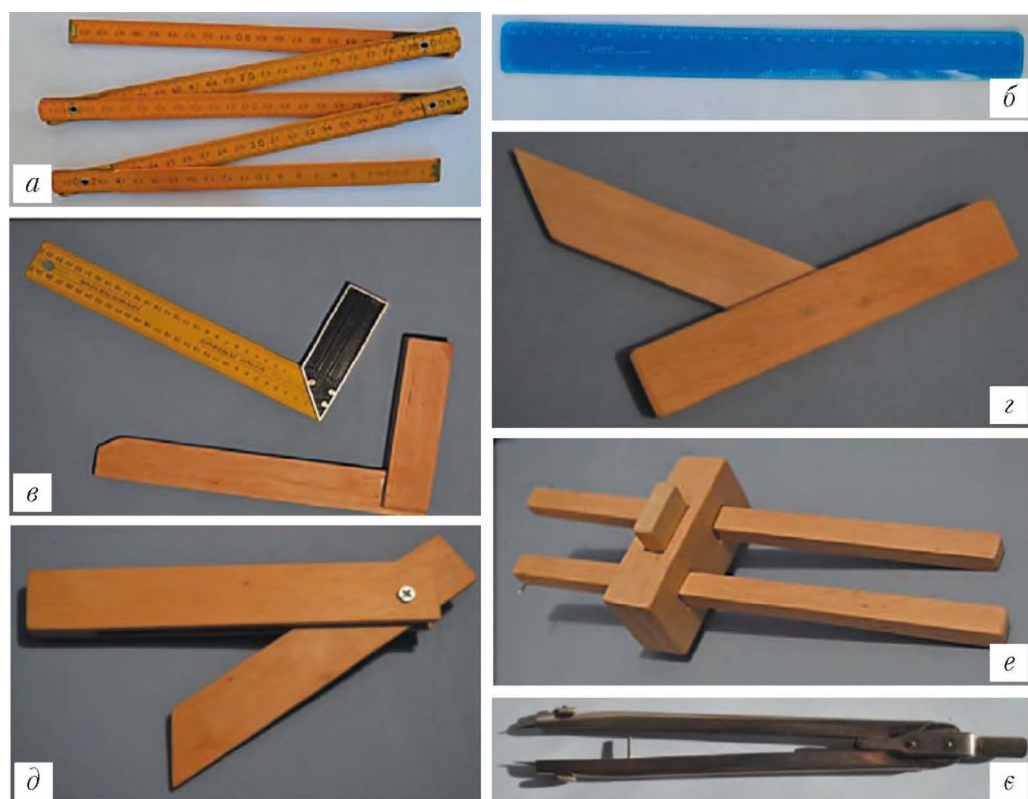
Розмічальні інструменти: а – метр столярний; б – лінійка; в – кутник; г – ярунок; д – малка; е – рейсмус; є – циркуль
